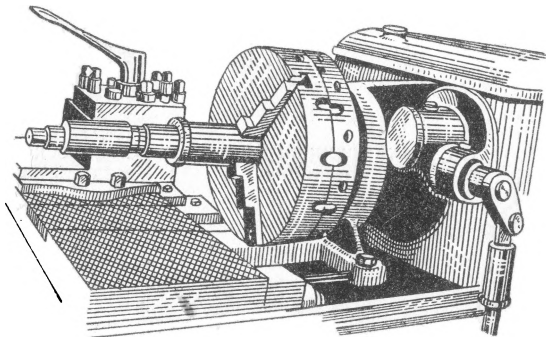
Спиральный трехлапчатый патрон с конической зубчатой передачей.
